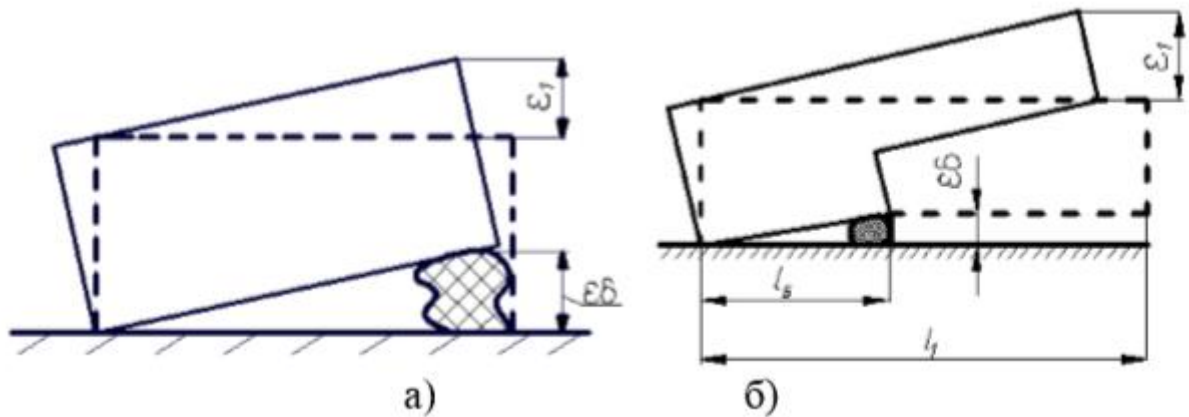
Влияние погрешности базирования на положение поверхностей заготовки
